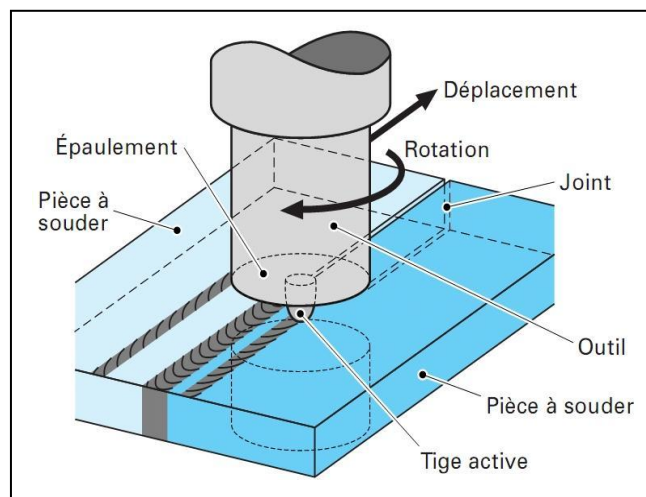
Présentation du soudage par friction malaxage. [3]
